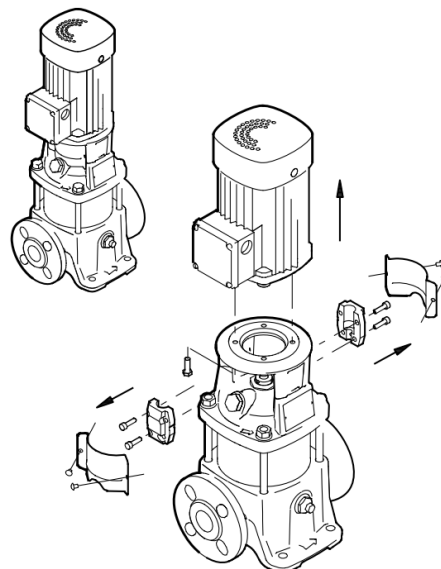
Демонтаж защитного кожуха и полумуфт
